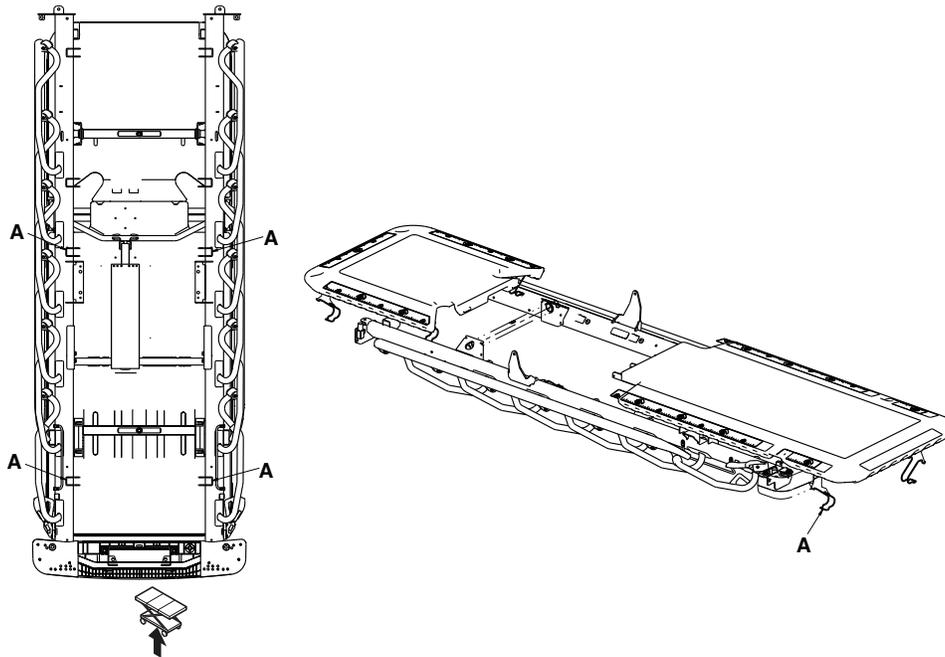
Remplacement du panneau de radiographie - côté pieds
